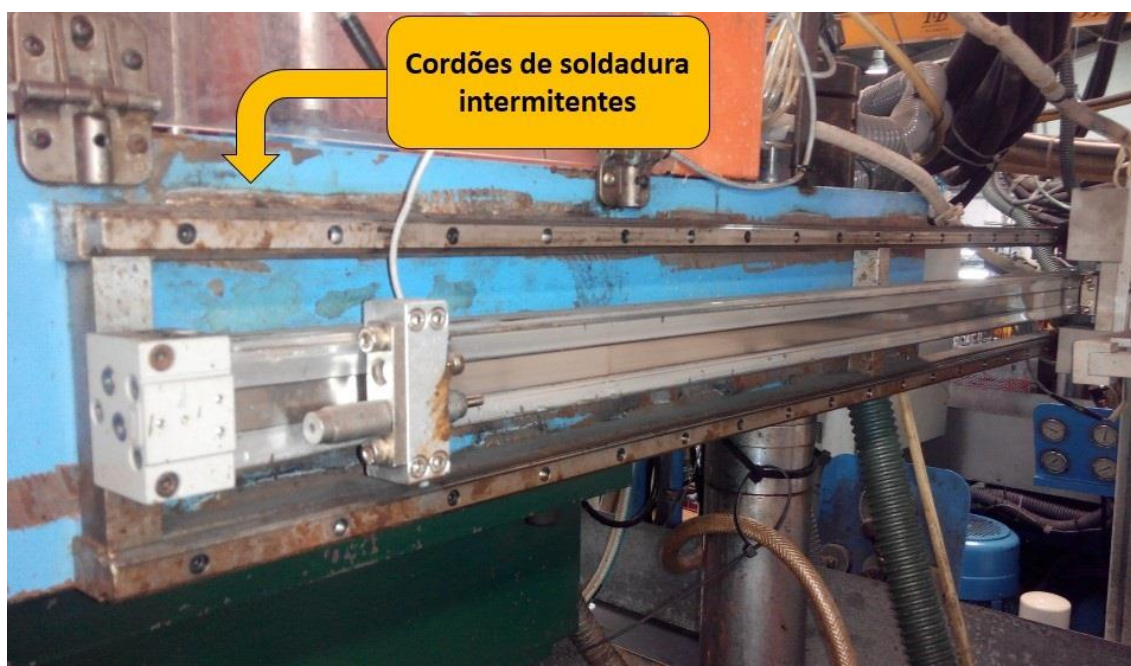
Transfer* soldado na cabeça da injetora.
